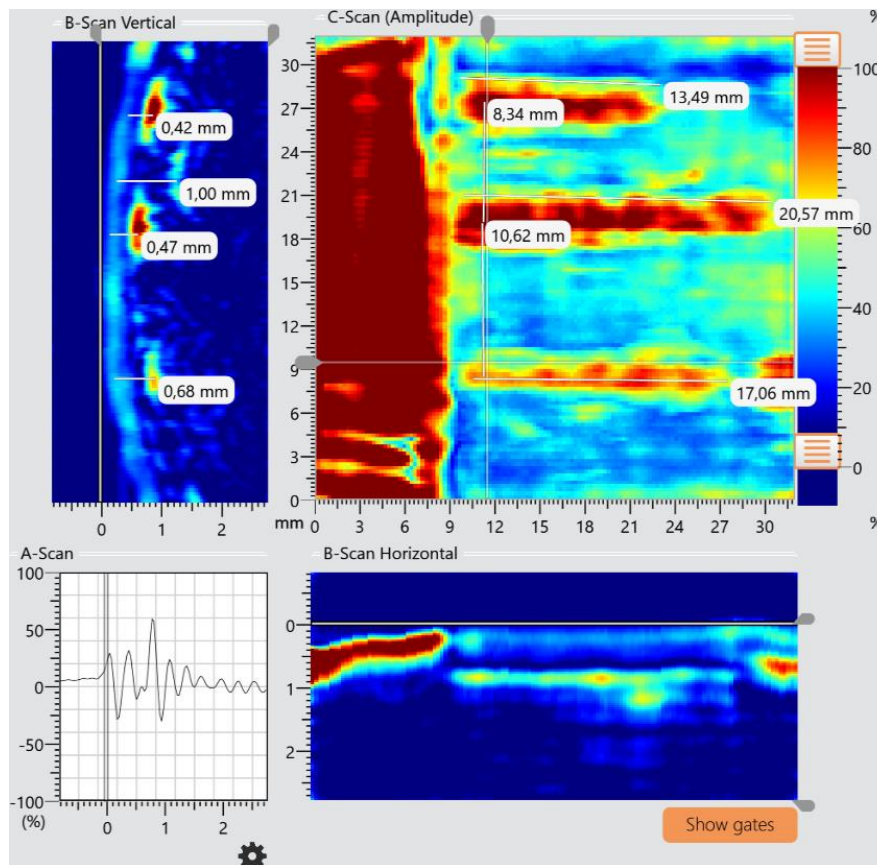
Obraz poloviny obloukového defektu na obrázku 39 ze spodní strany. B-skeny ukazují díru v odraženém signálu zadní stěny.
